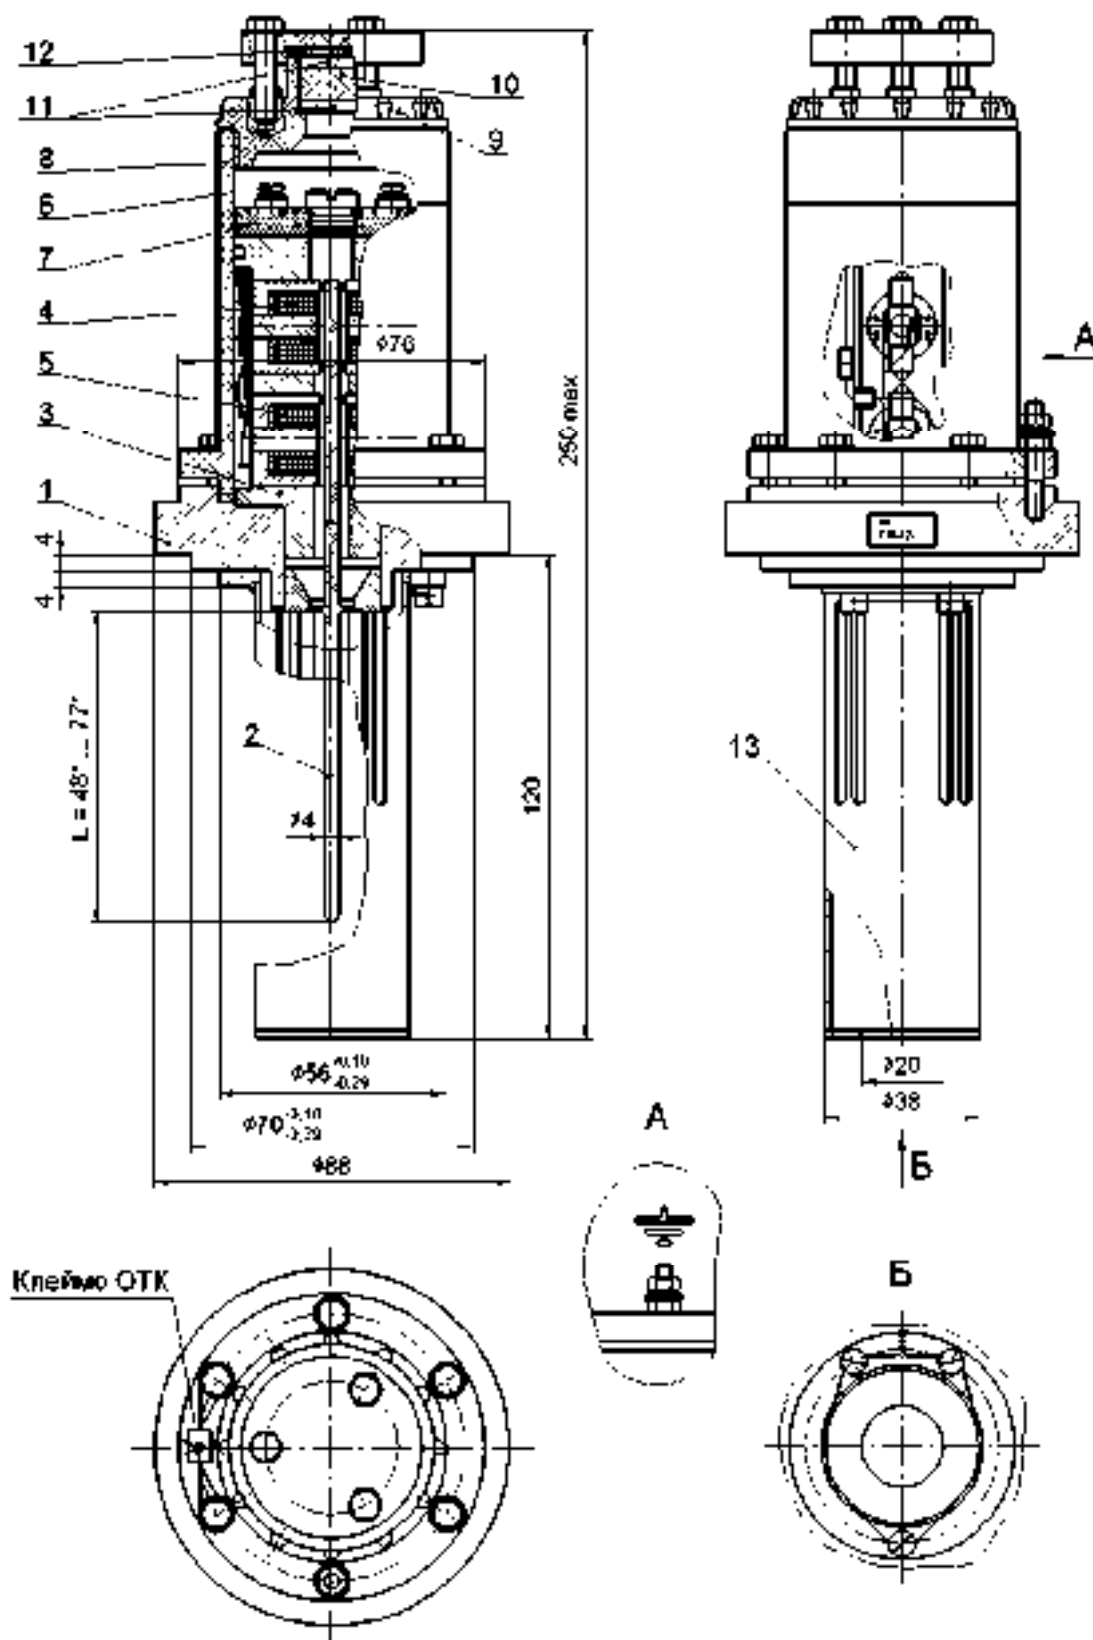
Внешний вид и габаритные размеры блока БЭ-63 вискозиметра
